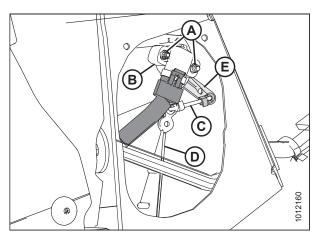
Assemblage du capteur de hauteur de la plateforme – Côté droit
